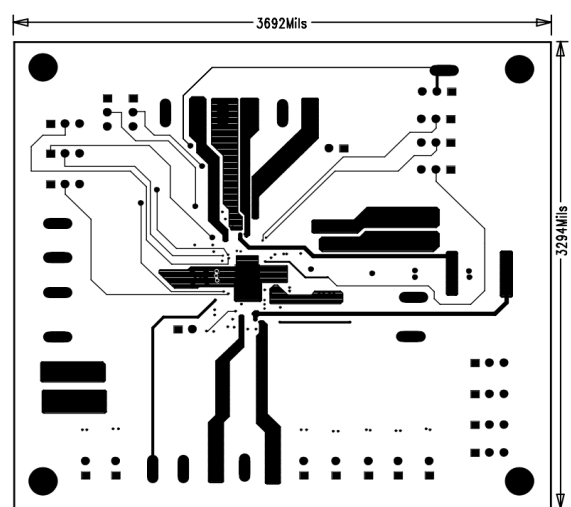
Max 8662 PCB LayOut - Bottom Layer 6.
